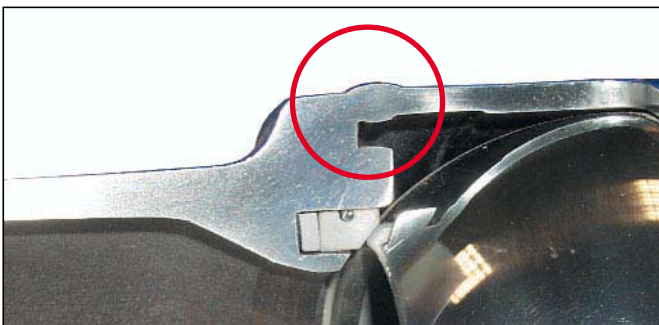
Schweissnaht Böhmer Kugelhahn
